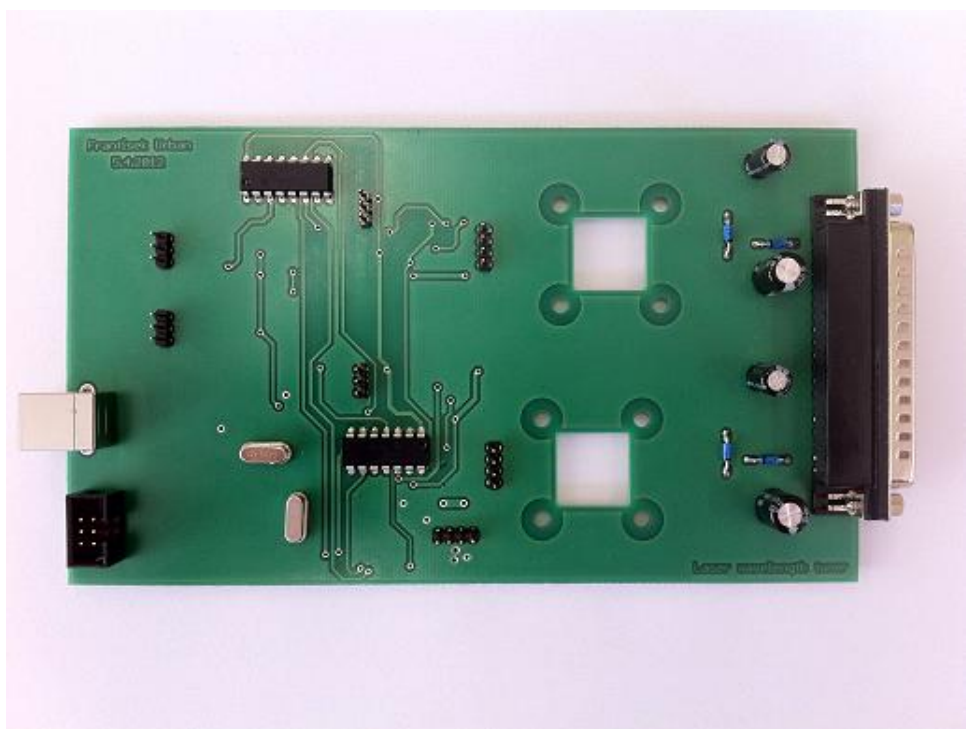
b) Deska plošného spoje pohled Bottom
